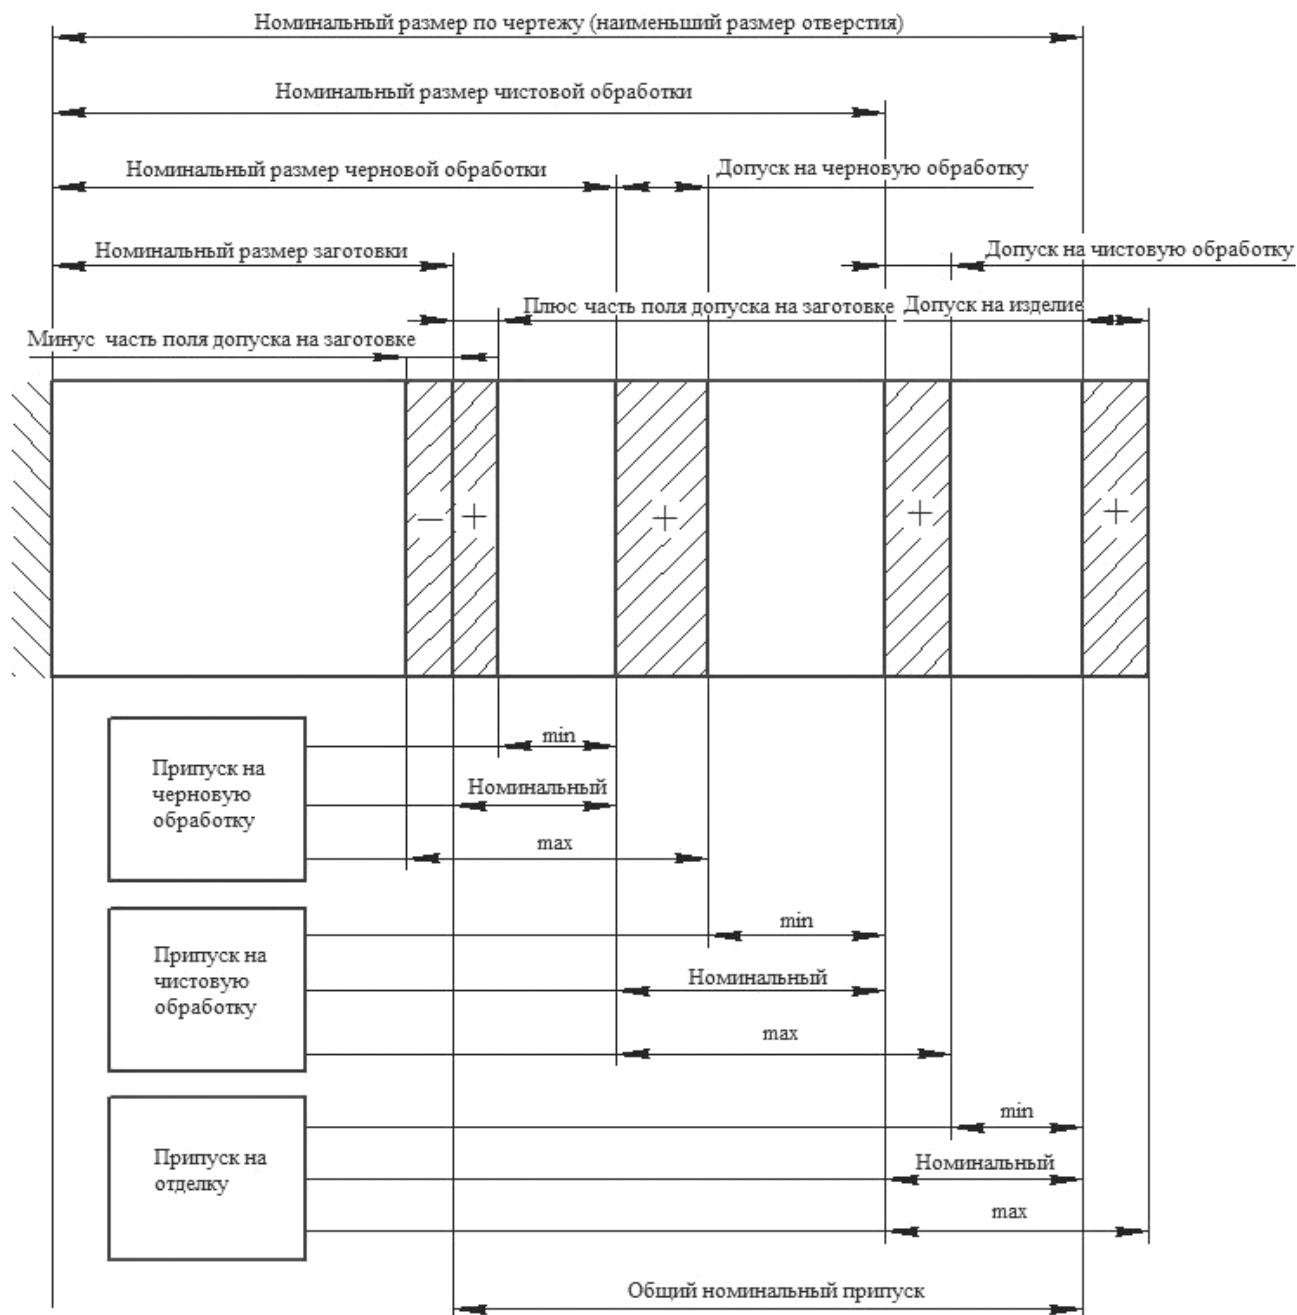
Схема расположения операционных припусков и допусков на различных стадиях обработки для внутренних поверхностей (отверстий)
